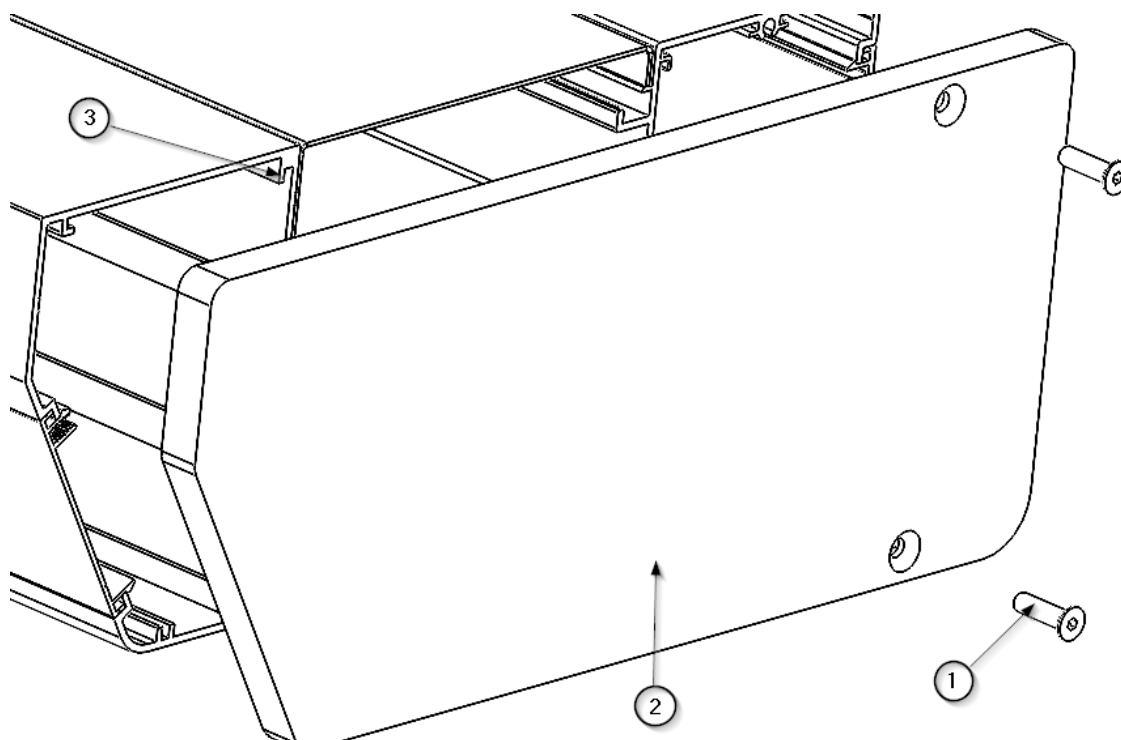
Démontage / montage des embouts sur le corps principal TOR
